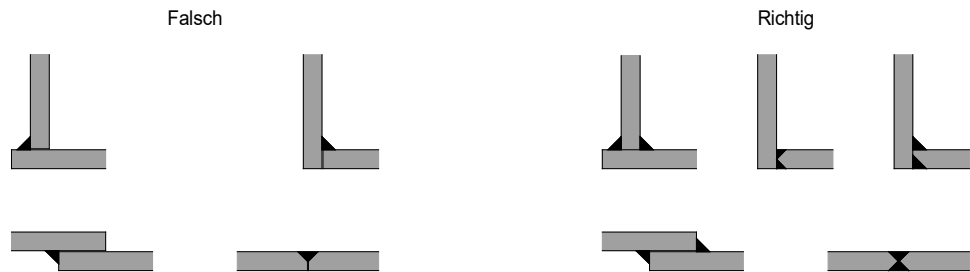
Ausbildung von Schweissnähten.
